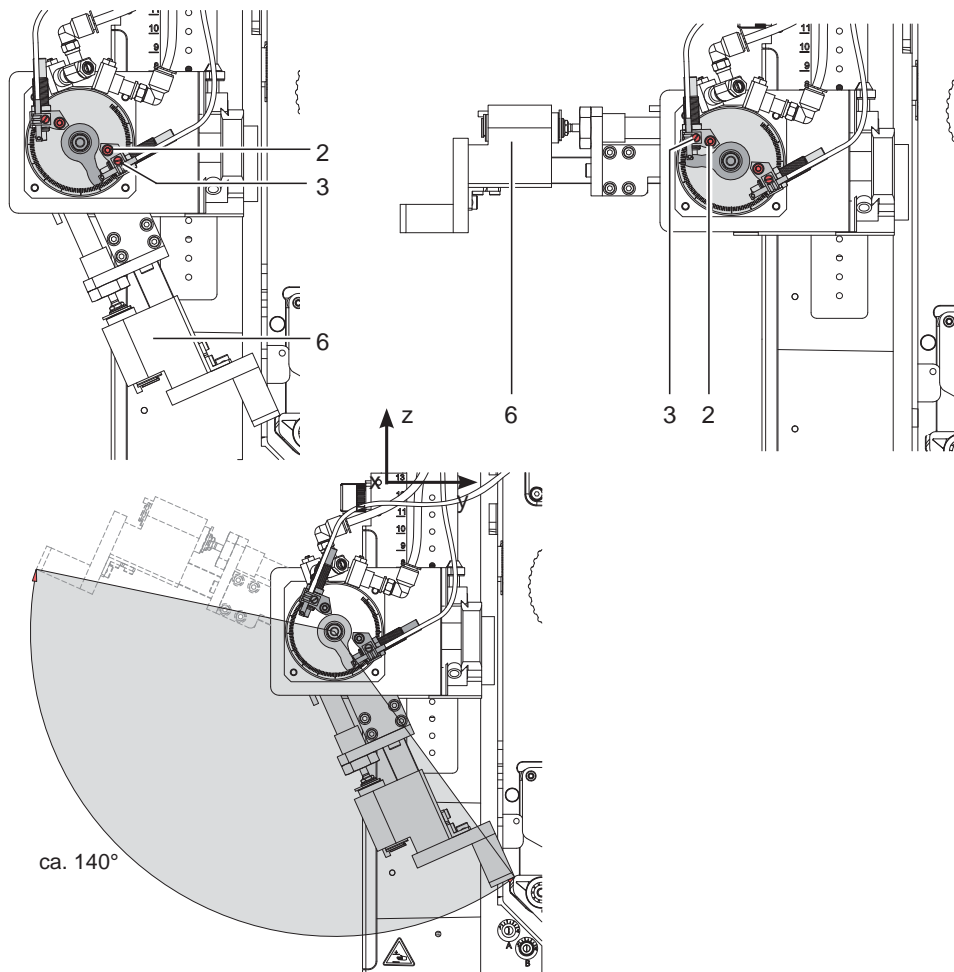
Justage des Schwenkbereiches der Stempelbaugruppe
